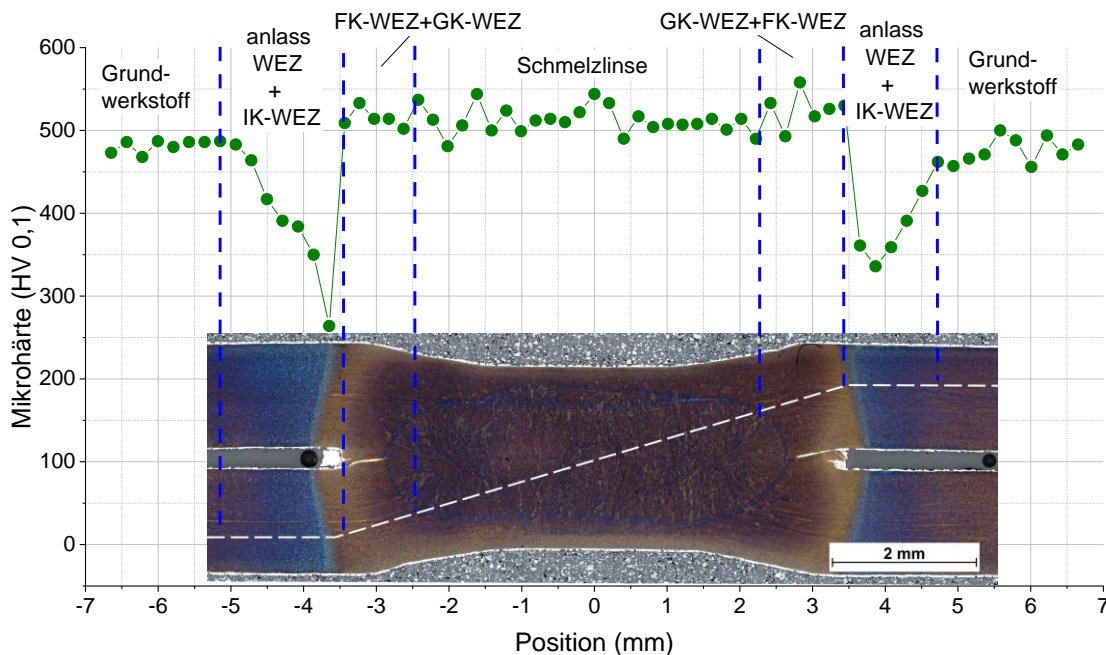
Härteverlauf und Schlibbild einer Widerstandspunktschweißverbindung aus 22MnB5 mit einem Zweiimpuls-Schweißparametersatz (MT aus [43])
